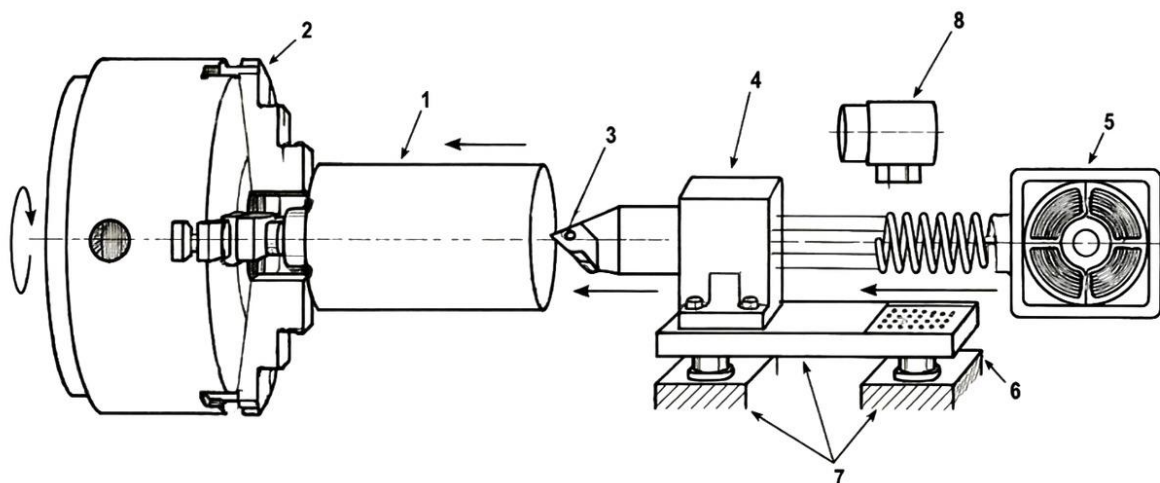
Схема работы системы Fast Tool Servo (1 – заготовка, 2 – шпиндель станка, 3 – алмазный резец, 4 – держатель резца, 5 – двигатель с голосовой катушкой, 6 – механизм гибких шарниров, 7 – подшипник воздушной подушки, 8 – лазерный датчик перемещения)
